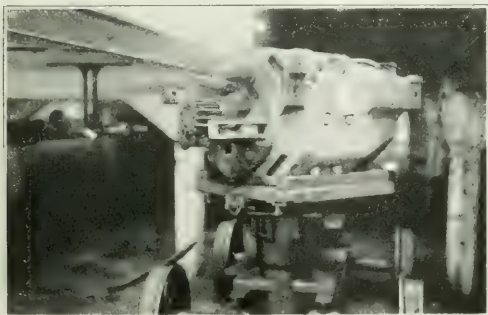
CARRETILLA CON GATO PARA FOSO. BAJANDO EL MOTOR
